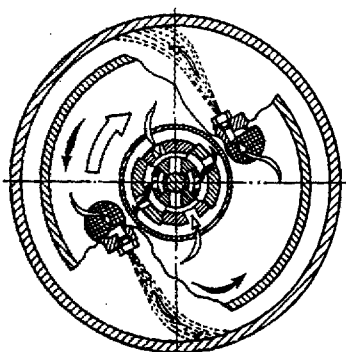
Схема действия реактивной центрифуги: 1 – корпус; 2 – колпак; 3 – стакан корпуса ротора; 4 – ось корпуса ротора; 5 – стакан, отделяющий полости очищенного масла от неочищенного; 6 – отверстия отвода очищенного масла; 7 – предохранительная сетка; 8 – отверстия подвода неочищенного масла; 9 – жиклер (сопло); 10 – трубка отвода очищенного масла; 11 – канал подвода масла от насоса
